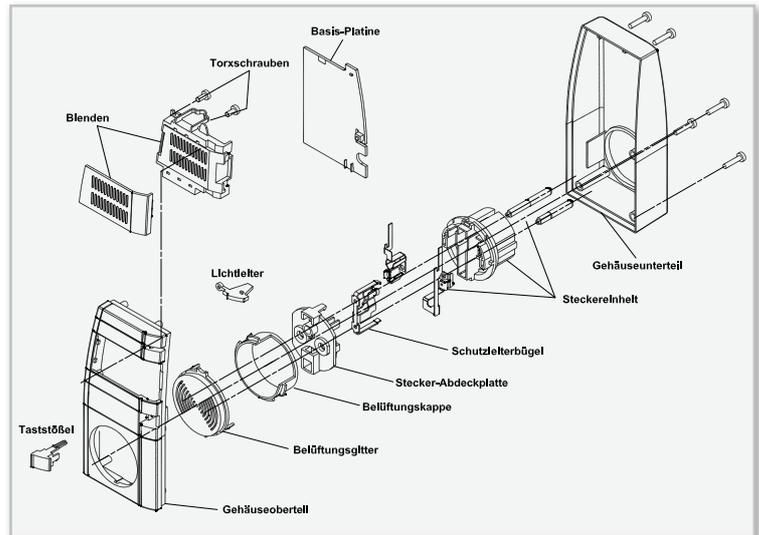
Explosionszeichnung des Gehäuses mit den Details zur Montage
